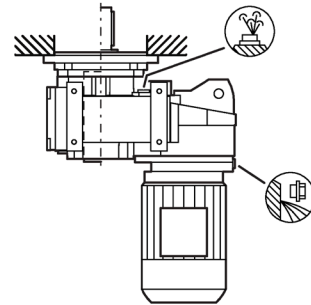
Einbaulagen für Flachgetriebe F.AD Aufsteckausführung Baugrößen 39 - 189
